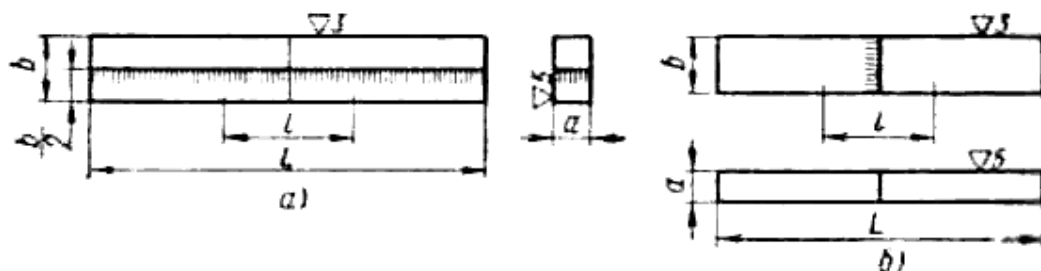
Форма образцов для испытания на изгиб при расположении сварного шва
